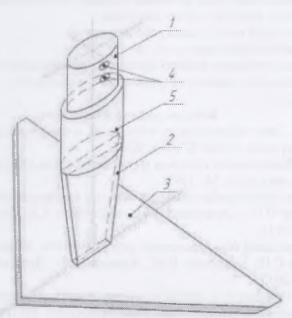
Общий вид рабочего органа почвообрабатывающей фрезы
